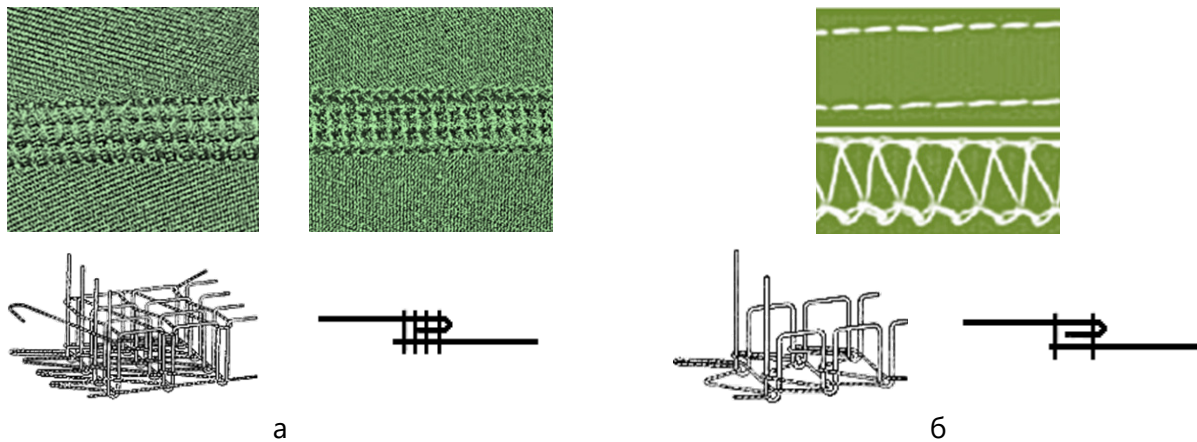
Зразки строчок: а- код стібка 607; б – код стібка 406
